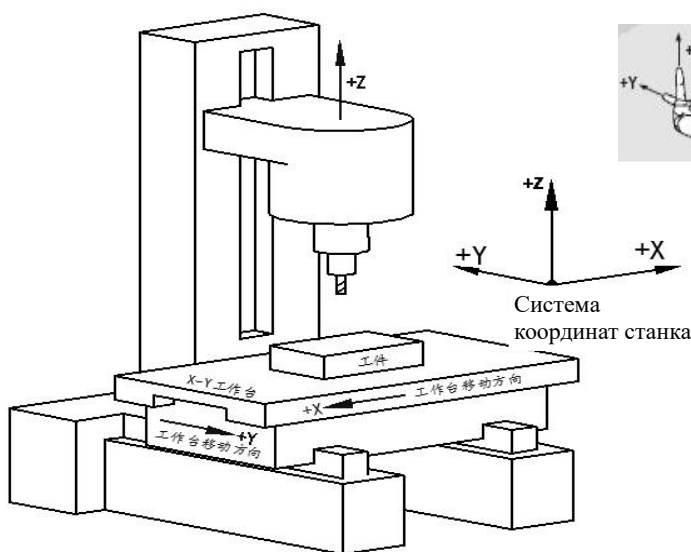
Вертикальный фрезерный станок с одной колонной
